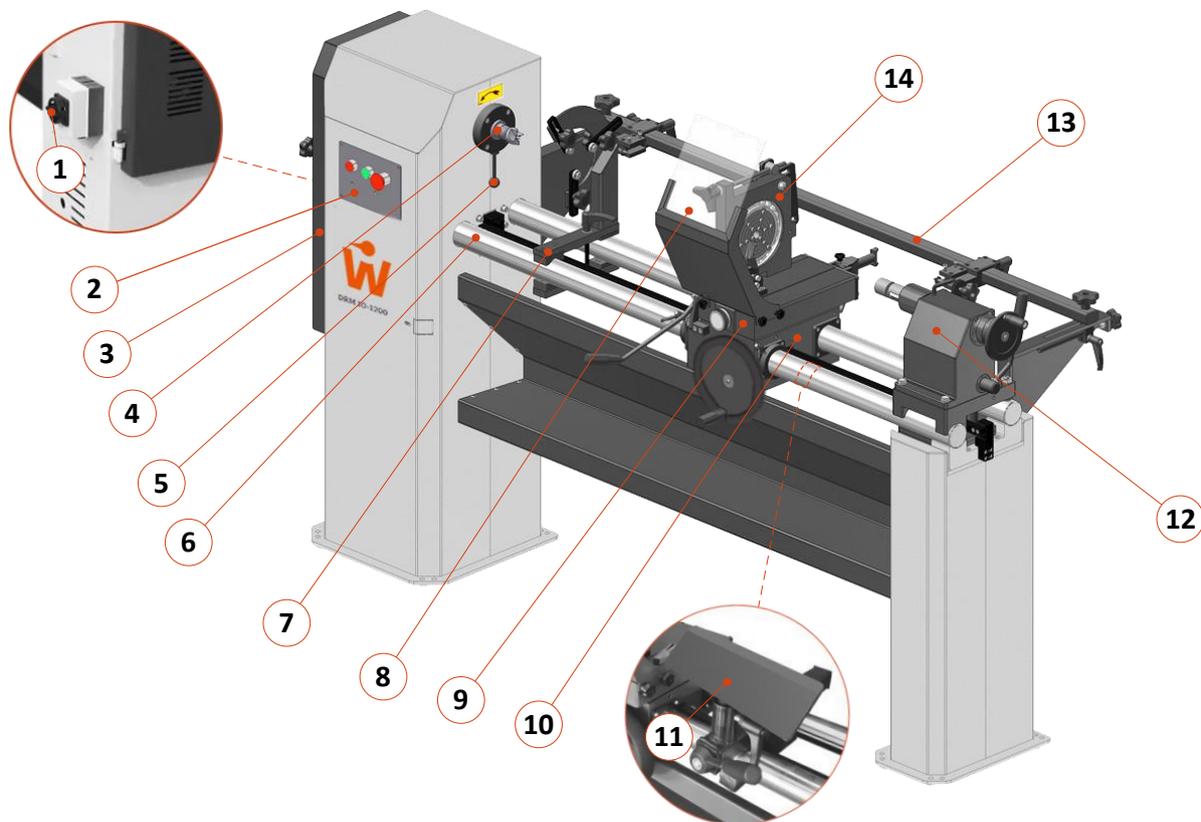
Maschinenübersicht - Hauptkomponenten
